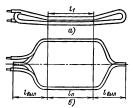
Қатушка двухслойной обмотки статора. Общий вид.
